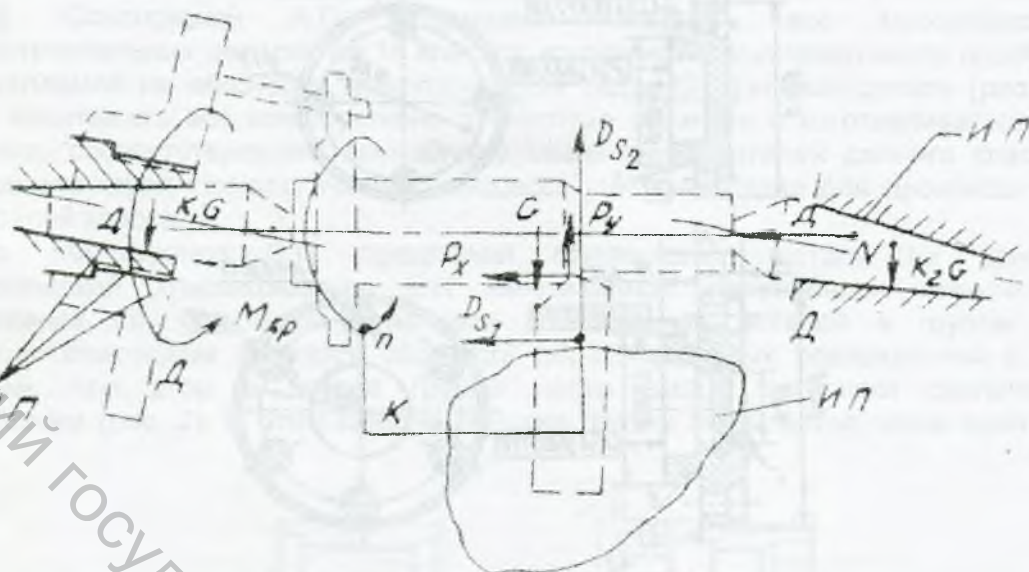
Проявление служебного назначения станка в исполнительных поверхностях:
